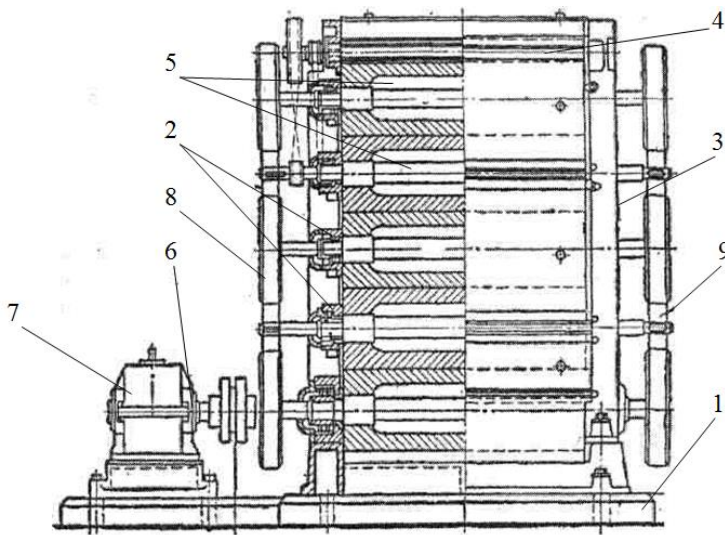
П'ятивальцьовий верстат ВС-5: 1 – рама; 2 – підшипники; 3 – станина; 4 – живильний валок; 5 – робочі валки; 6 – редуктор; 7 – електродвигун; 8 і 9 – шків.
